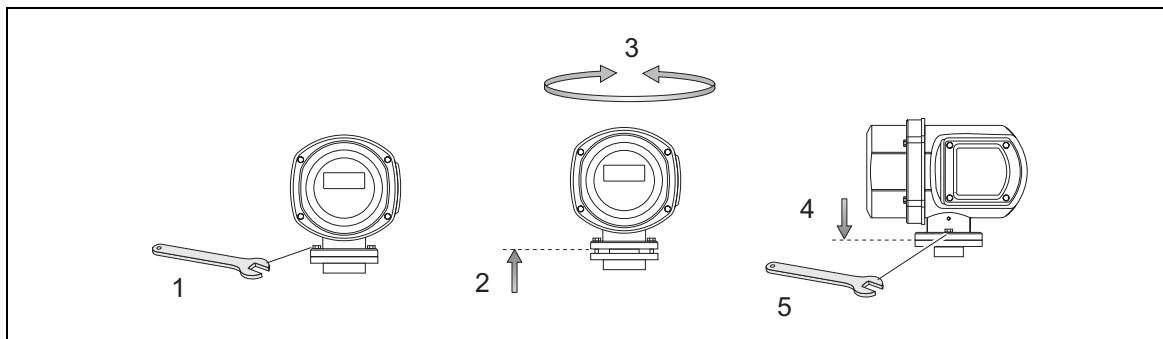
Поворот корпуса преобразователя (в рабочем корпусе из нержавеющей стали)
